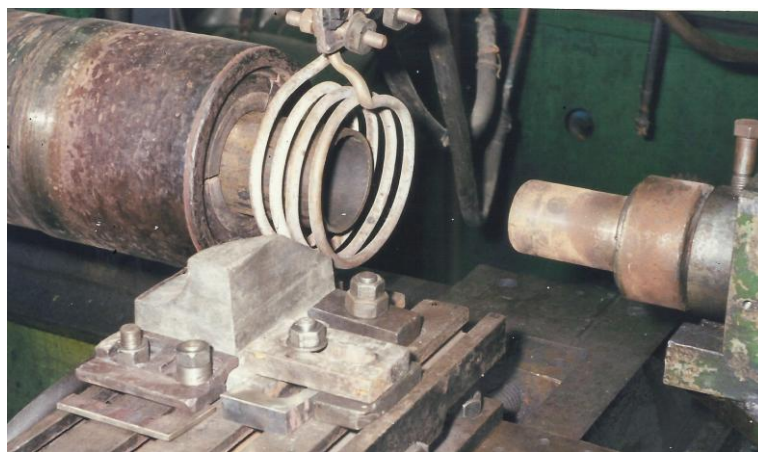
Індукційне нагрівання трубної заготовки перед обкочуванням ІТ
